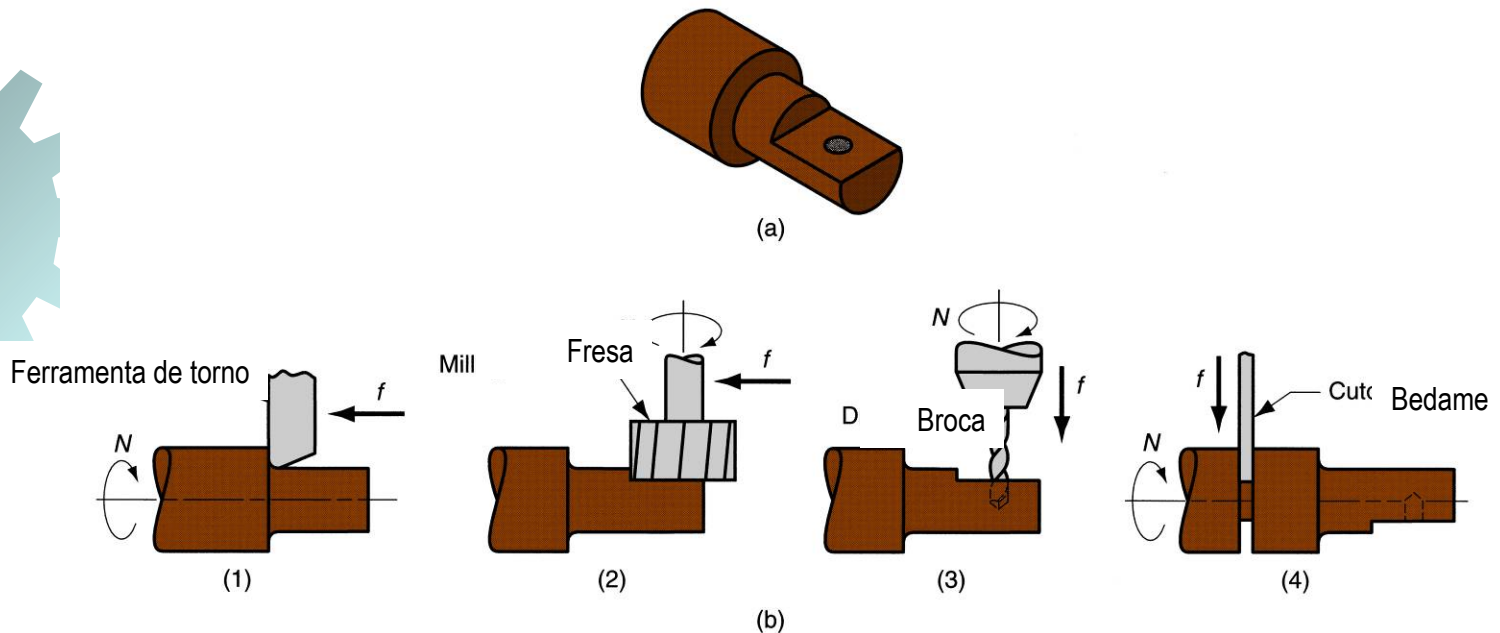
Operação de um centro de torneamento: (a) exemplo de peça com superfícies torneadas, fresadas e furadas; e (b) sequência de operações em um centro de fresamento: (1) torneamento do segundo diâmetro, (2) fresamento plana com peça na posição angular programada, (3) furação da peça na posição programada e (4) sangramento da peça para retirá-la da peça bruta .
